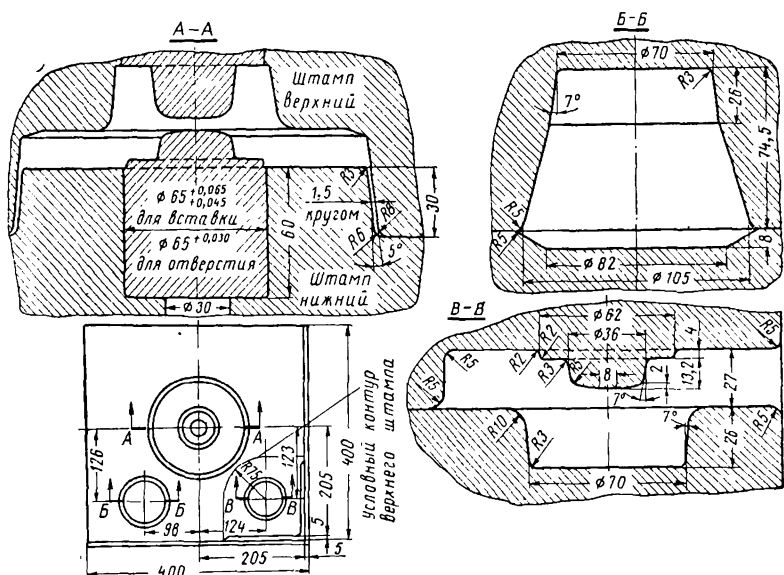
Закрытый молотовый штамп для поковки шестерни
